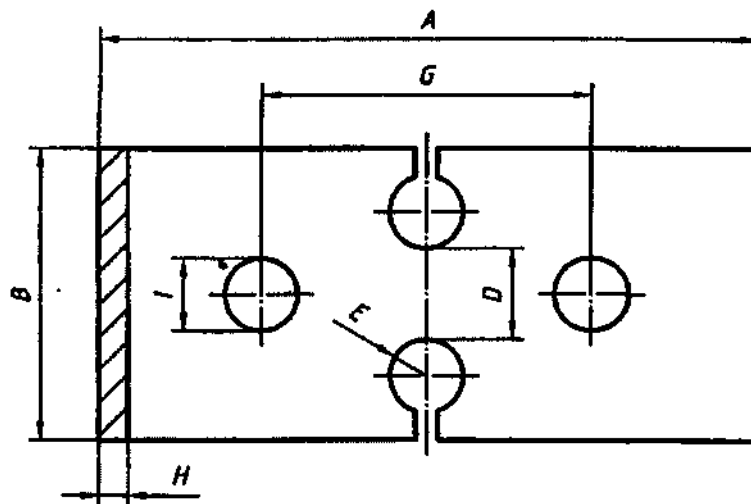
Зразок типу А для випробування на розтяг, виготовлений методом механічної обробки (при $e < 25$ мм)
